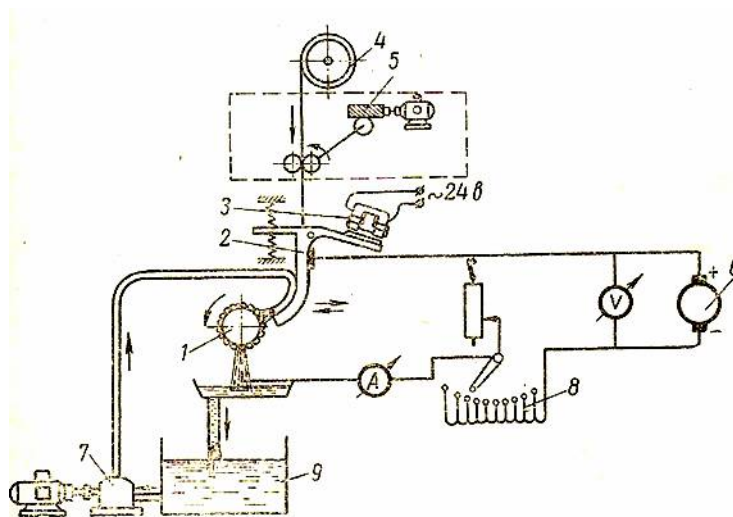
Схема установки для вібродугової наплавлення.
